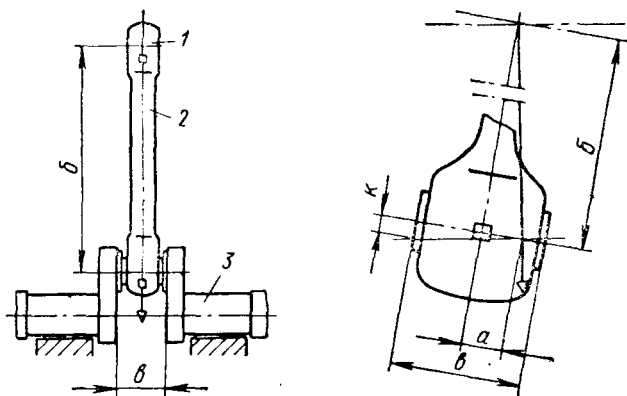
Схема проверки перпендикулярности осей шатуна и шатунной шейки вала:
